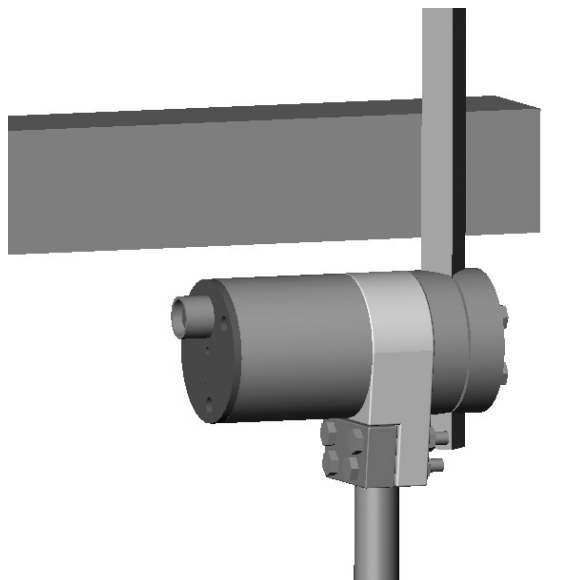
Fissaggio del sensore sotto il braccio delle pale di raschiamento
